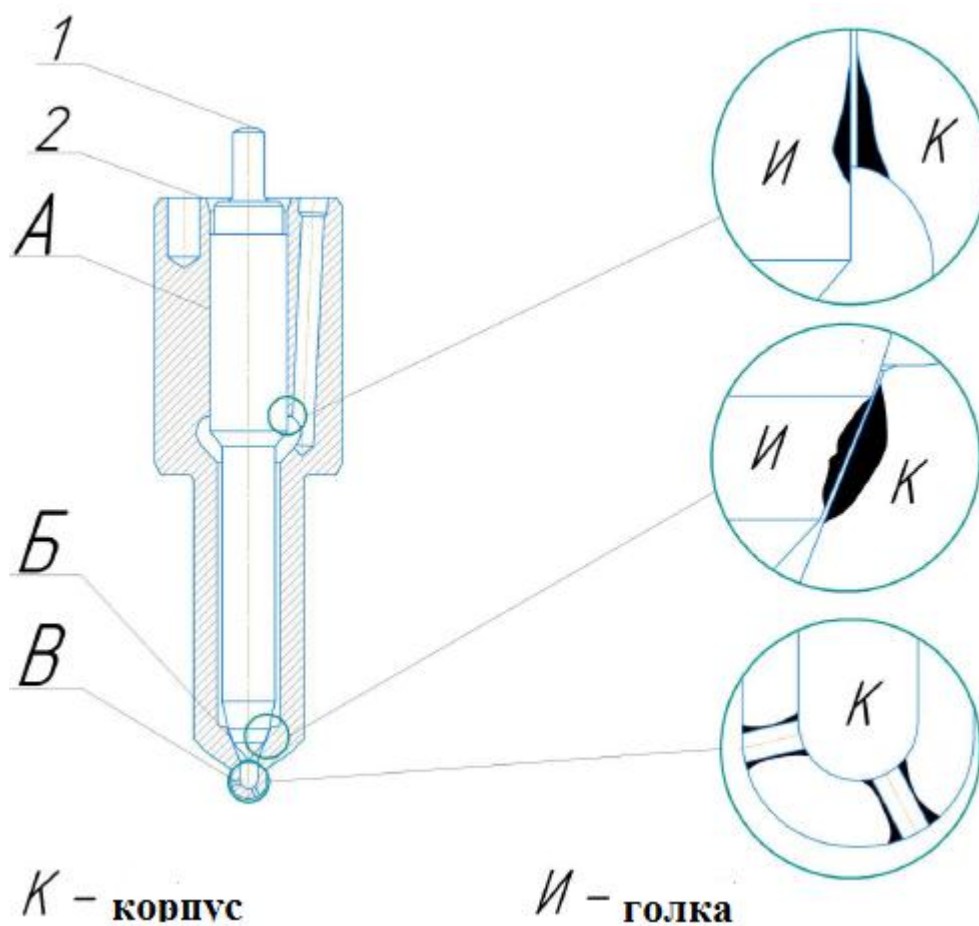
Дефекти (знос) голки та корпусу розпилювача [21]: 1 – торець голки; 2 – торець корпусу розпилювача; А - напрямна поверхня; Б - замикаючий конус; В – отвори, що розпилюють.
